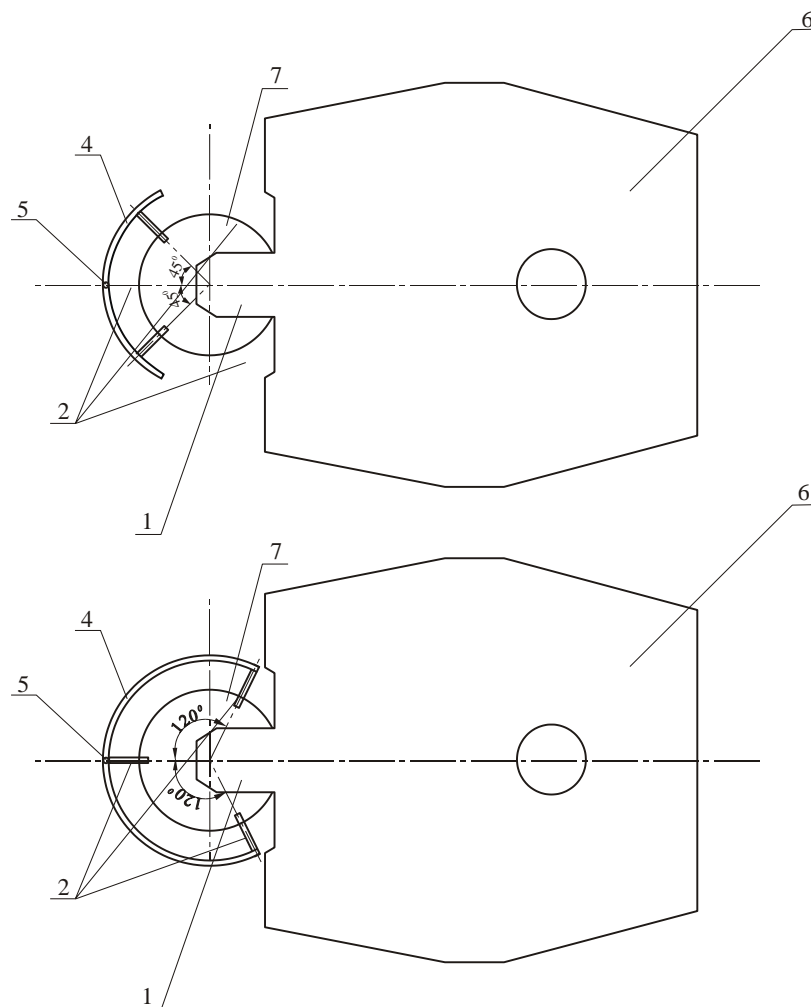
Схема расположения двух и трех сопел над ковшом вид сверху:
